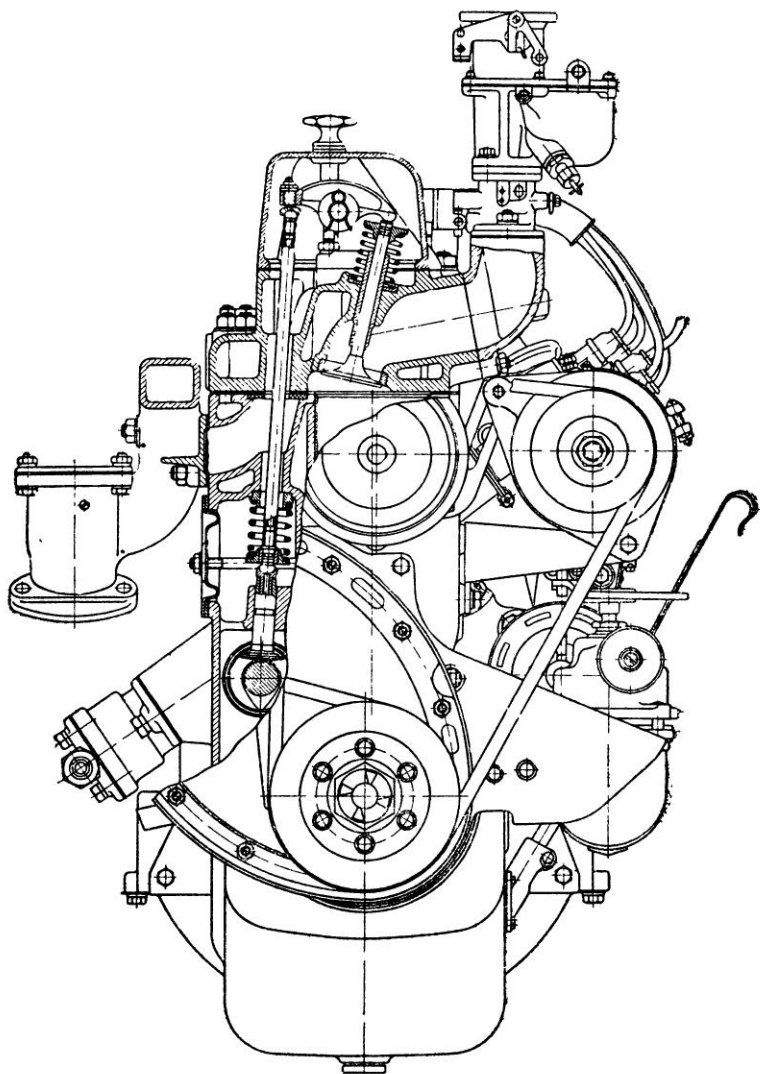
Поперечный разрез двигателя М-20, имеющего головку с верхними впускными клапанами
